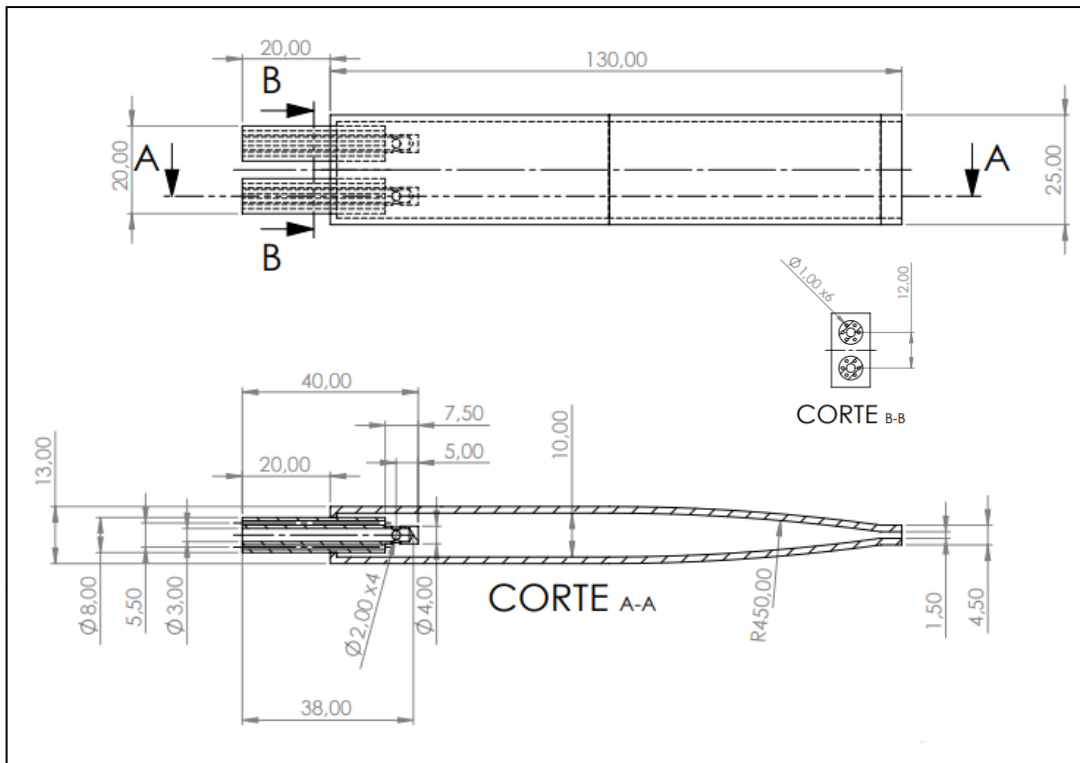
Desenho técnico do bocal utilizado na técnica de aplicação do MQL.
